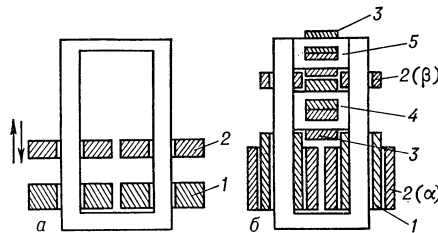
Схема сварочного трансформатора для дуговой сварки: а — с механическим регулированием индуктивного сопротивления и напряжения; б — с электрическим регулированием; 1 и 2 — первичная и вторичная обмотки; 3 — обмотка управления; 4 и 5 — среднее и верхнее ядро.
